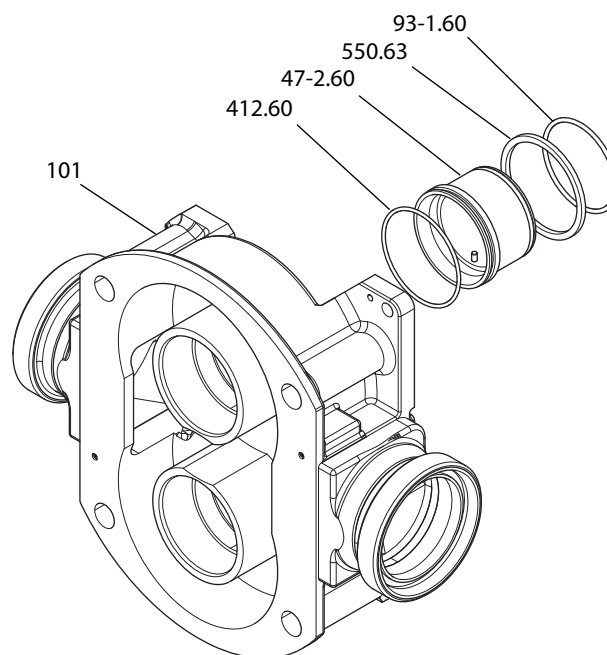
Premontaje del cuerpo de la bomba, caso de aplicación B
